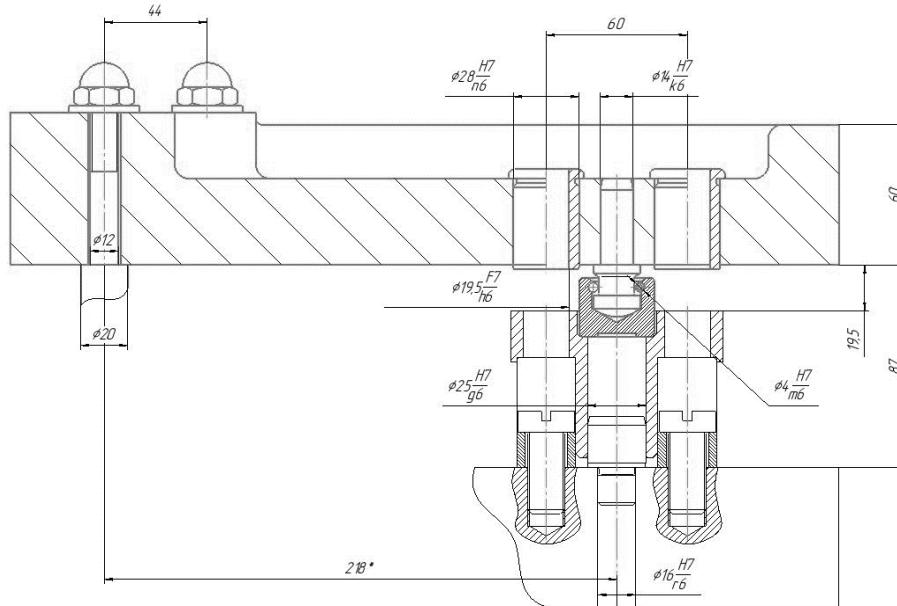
Чертеж заготовки, установочных элементов и зажимного механизма
